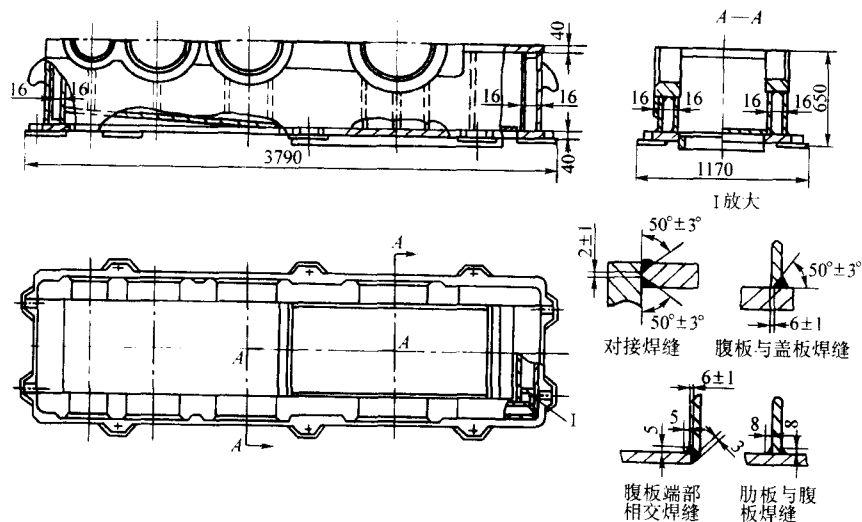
双层壁剖分式减速器下箱体的焊接结构
